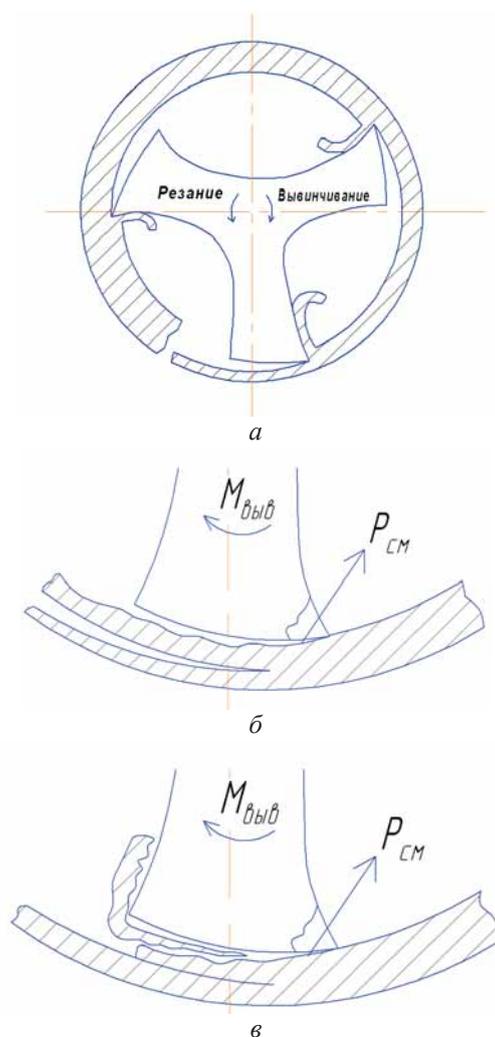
Схема нарезания резьбы метчиком: а – схема отделения стружки режущими зубьями метчика; б – взаимодействие зуба метчика с обрабатываемой поверхностью при его повороте на один угловой шаг зубьев; в – схема заклинивания зуба оторвавшимся элементом стружки
